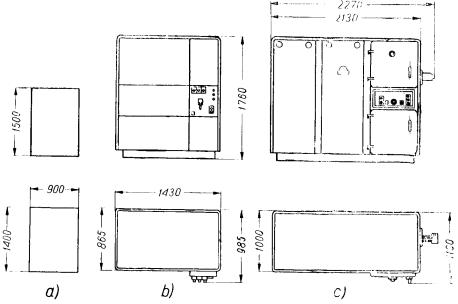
Aussenmasse des Mittelfrequenz-Induktionsofens Type PIS-20: a — Transformator, b — Gleichrichter, c — Generator
